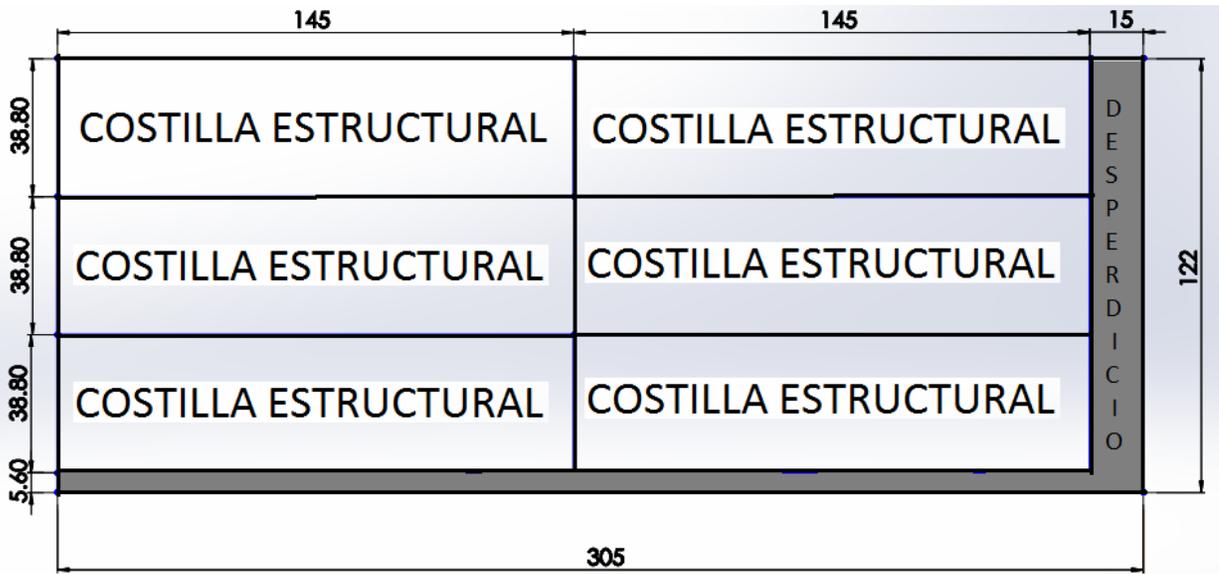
Plantilla de corte para costilla estructural (cotas en centímetros) (Fuente: CyRVR)
